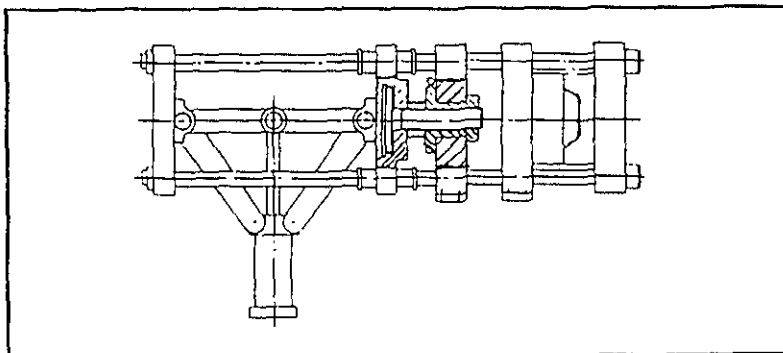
Cierre Hidromecánico Tipo Rodillera-Pistón
